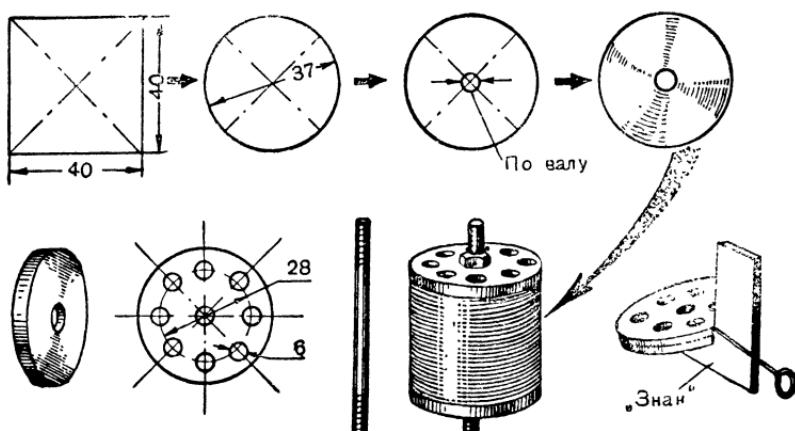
Наборный восьмиполюсный якорь с круглыми пазами.
